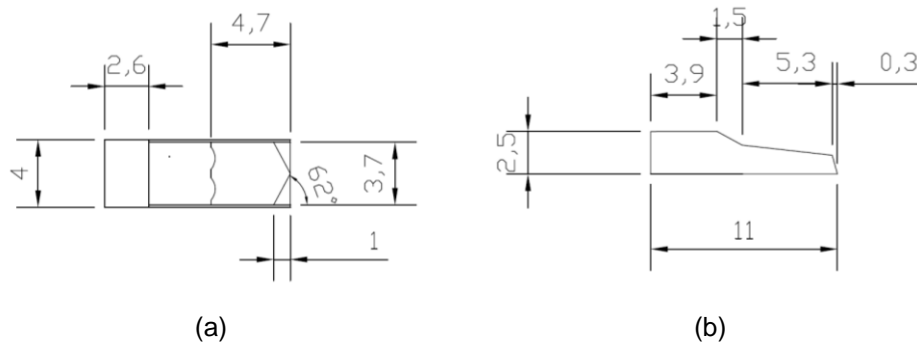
Dozer placa triangular (a) Vista en planta (b) Vista longitudinal.
